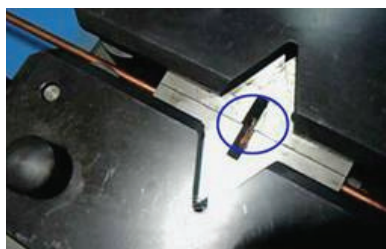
Установки холодной сварки Trex - YouTube:
